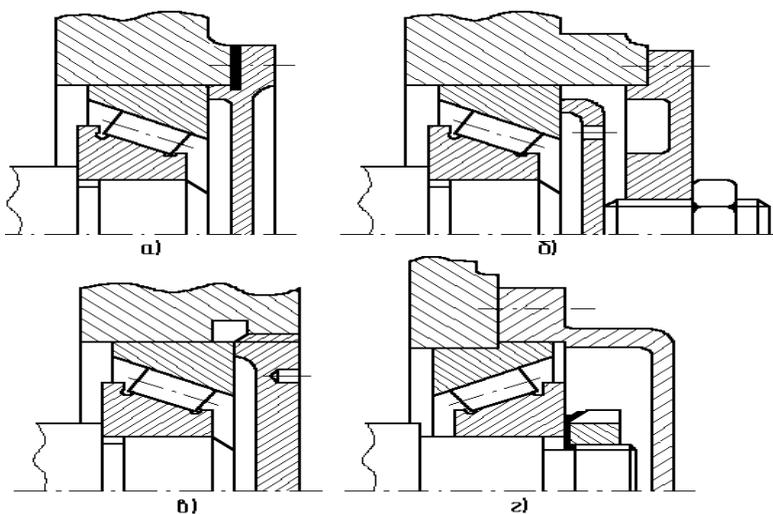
Способы регулирования зазора в конических роликоподшипниках:
